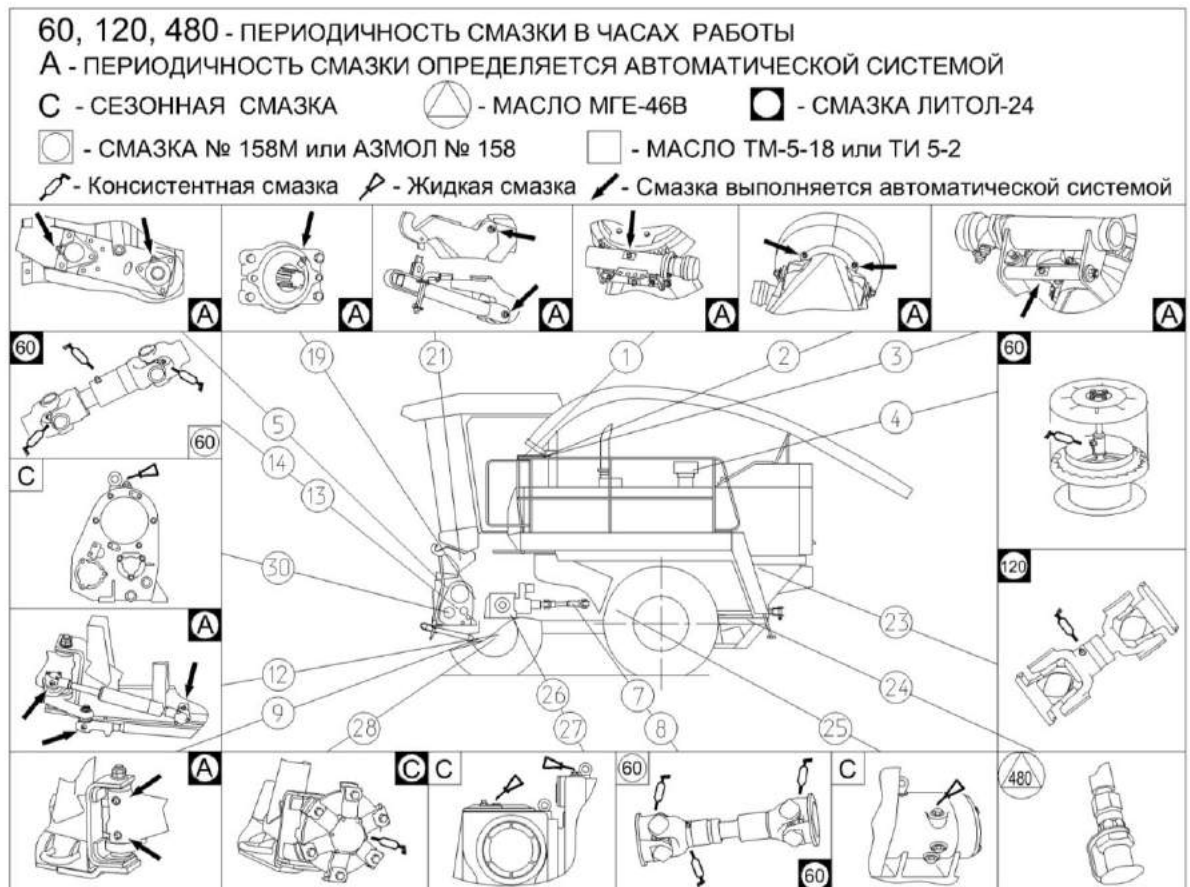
Схема смазки самоходного измельчителя (вид слева)
